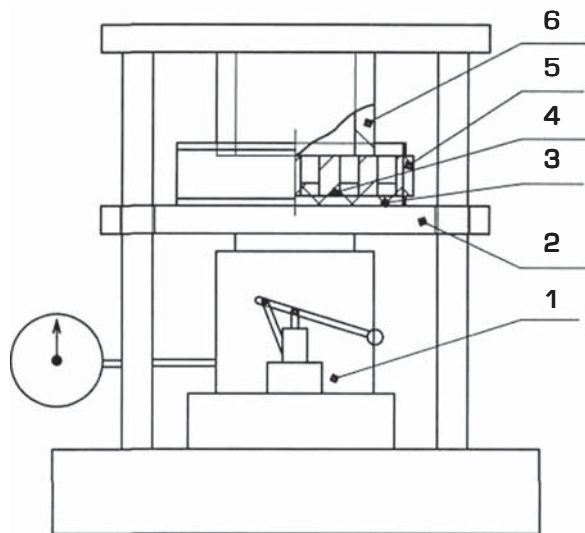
Лабораторный пресс: 1 – цилиндр пресса; 2 – стол пресса; 3 – слой смеси; 4 – ячеистый кокиль; 5 – опока; 6 – приспособление
